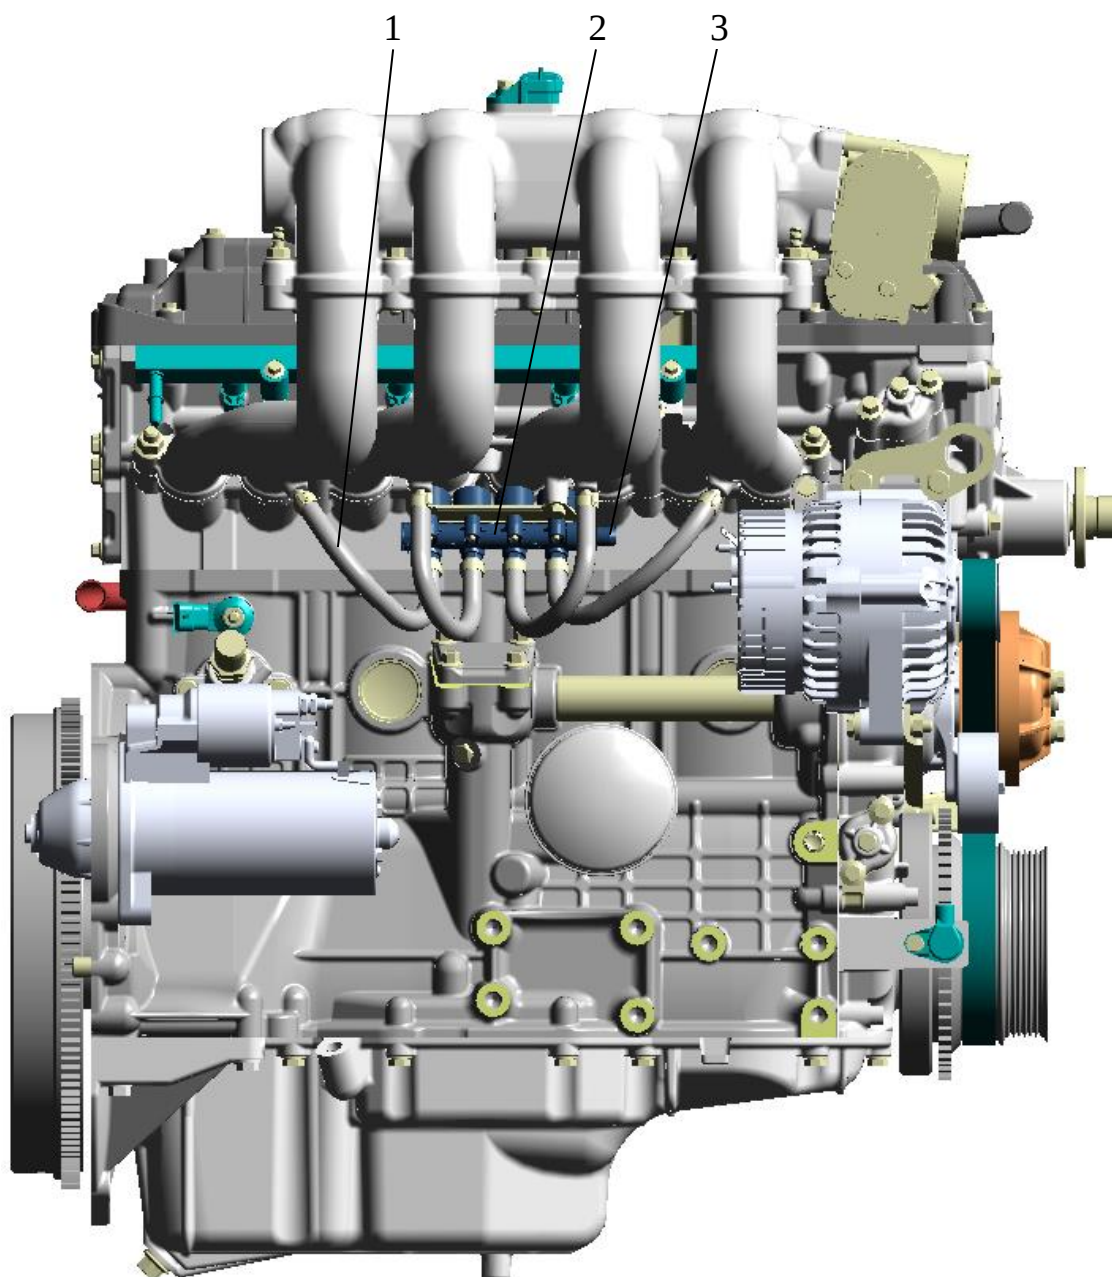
Вид двигателя ЗМЗ-409052.10 слева:
